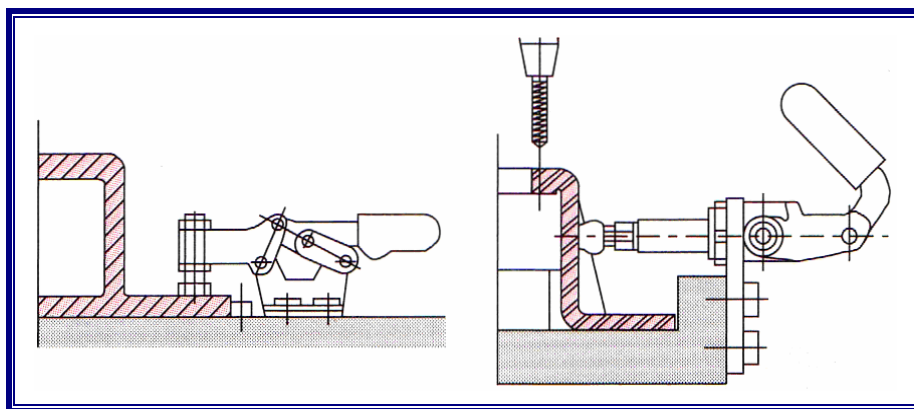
Sauterelles à levier horizontal et sauterelles à pousser
